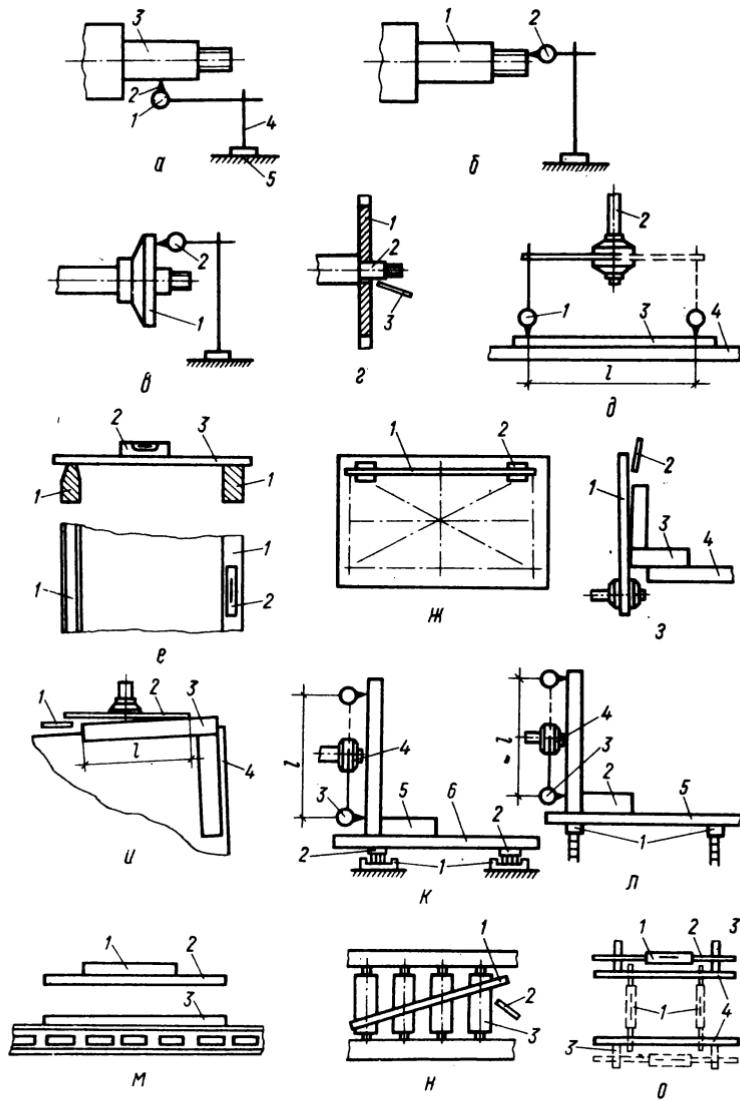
Схемы контроля состояния форматно-обрезного станка
